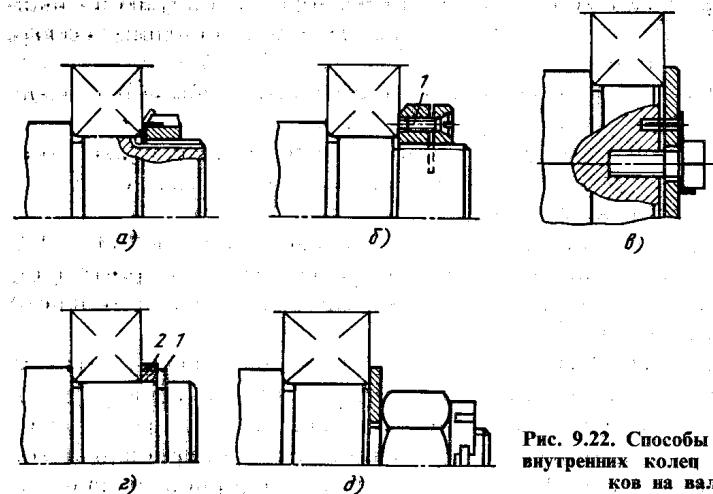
Способы крепления внутренних колец подшипников на валу
